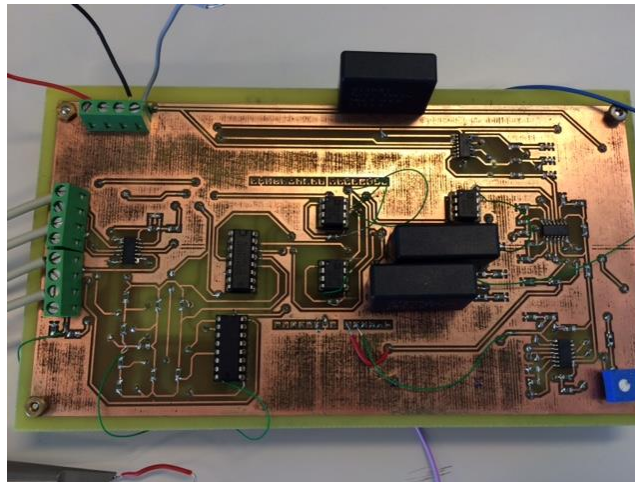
Circuito impreso soldado con los ajustes necesarios para el correcto funcionamiento.
